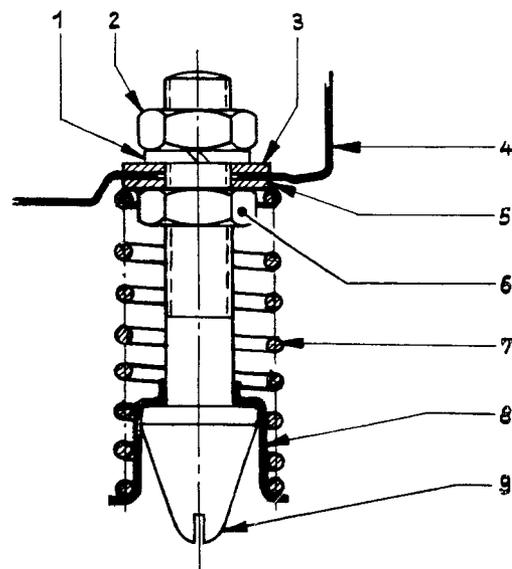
Befestigung des Führungszapfens an Motorhaube
